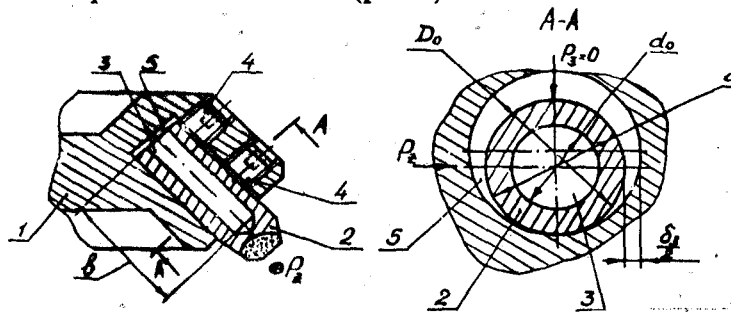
Торцевая фреза с цилиндрической режущей вставкой
